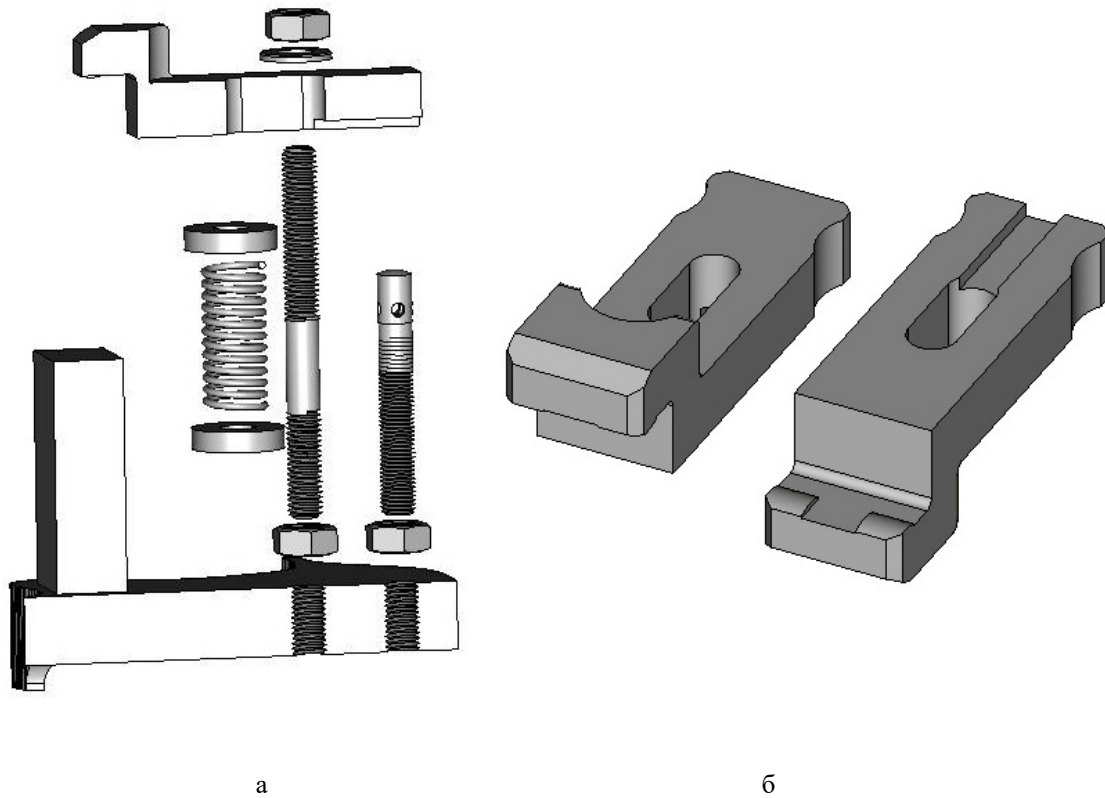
Детали зажимного устройства с прихватом ступенчатым:
